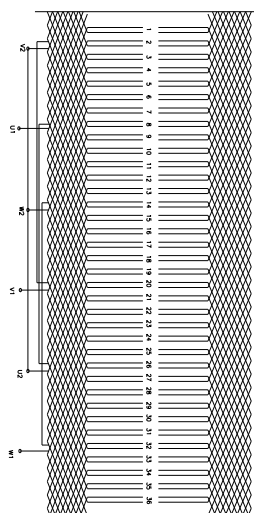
Схема соединения обмотки статора двигателя JD332 по норме
